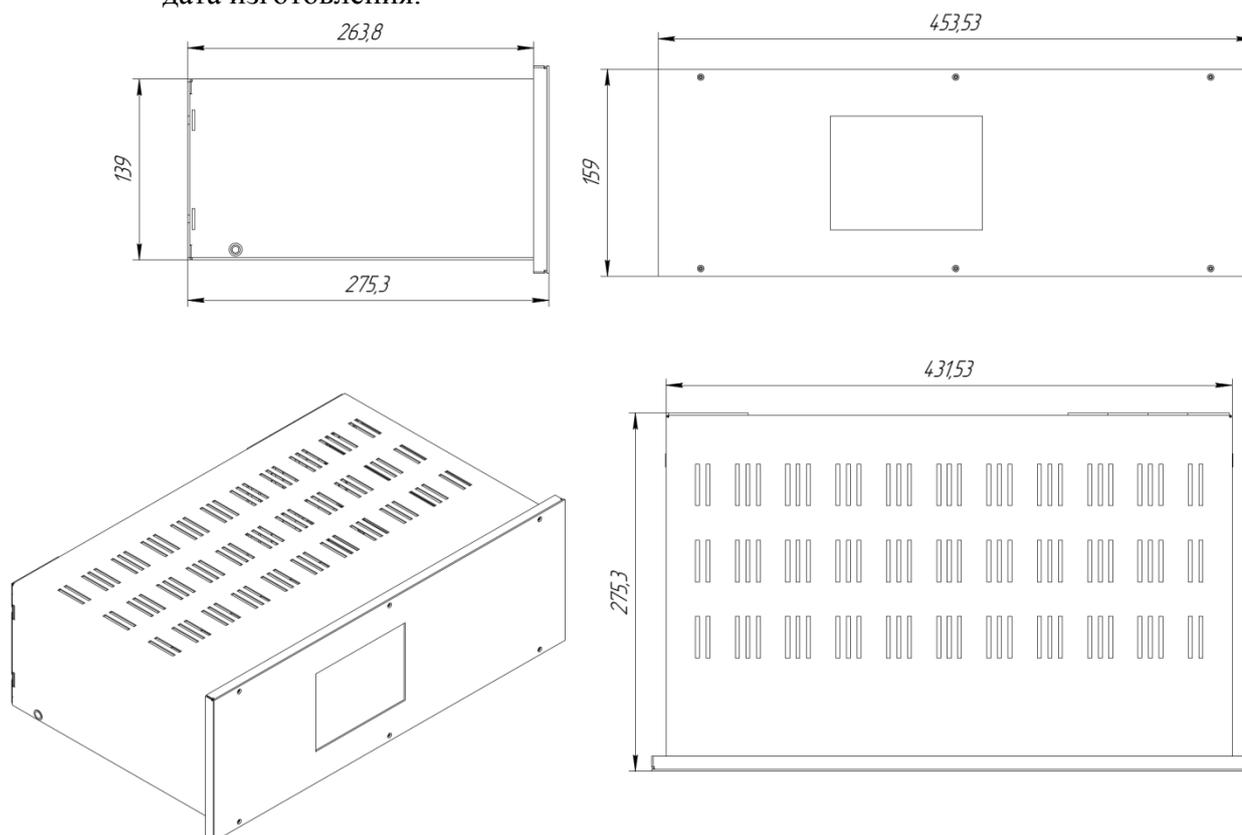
Габаритные размеры корпуса приёмопередатчика
